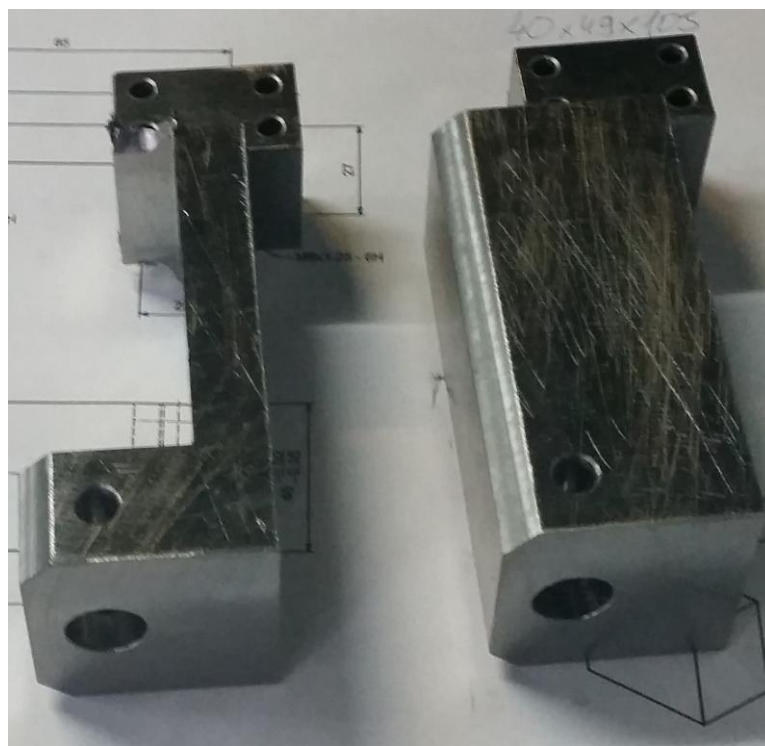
Изготовленные кронштейны специальные с использованием фрезерного обрабатывающего центра
